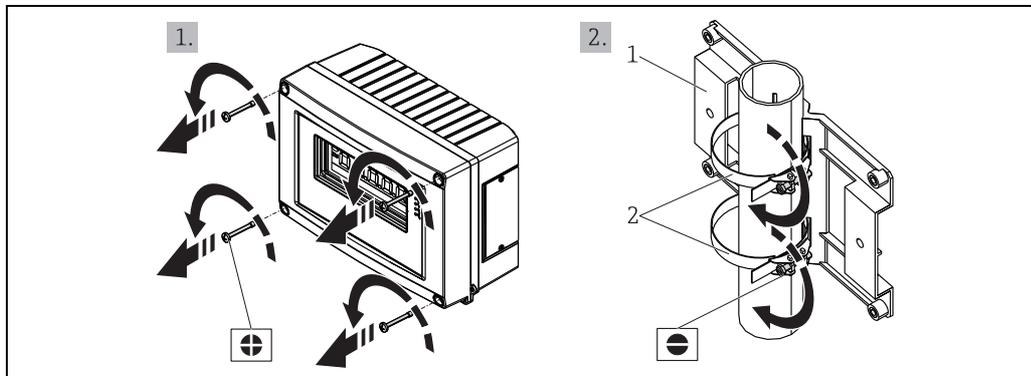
Montaggio del visualizzatore da campo su tubo con staffa di montaggio, passaggi a-b
